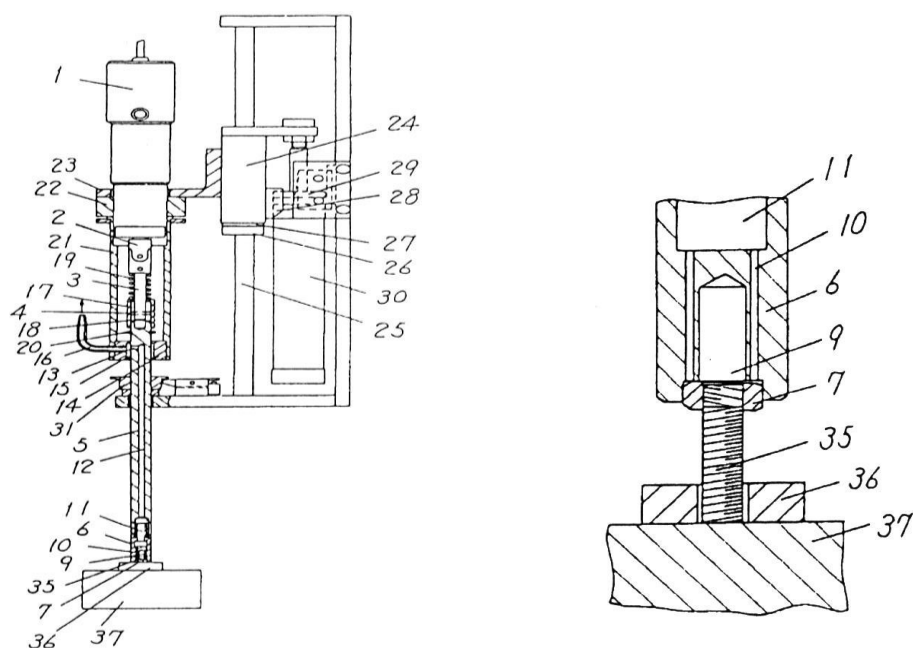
Автоматичний пристрій для загвинчування гайок: 1- електропривід; 5- шпindelь; 6- головка; 7- нагвинчувана гайка; 10, 11, 12- повітроканали; 16- відсмоктувальний штуцер; 35- шпилька.
